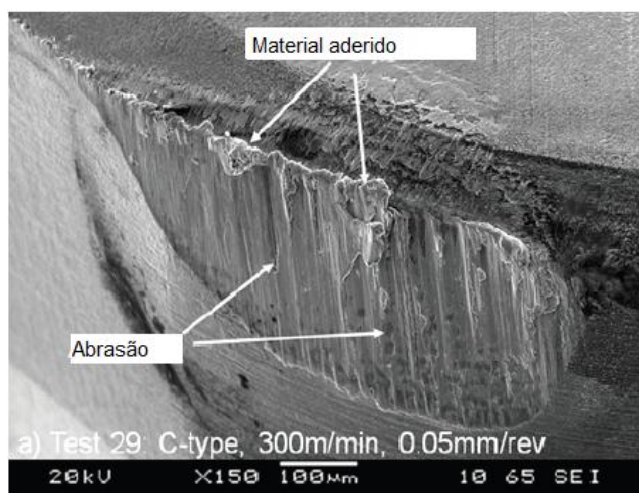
Imagem de MEV de desgaste de entalhe da liga de níquel Inconel 718 com ferramenta de PCBN sem revestimento com $v_c = 300$ m/min, $f = 0,05$ mm/rot e $a_p = 0,2$ mm (KHAN et al., 2012).
